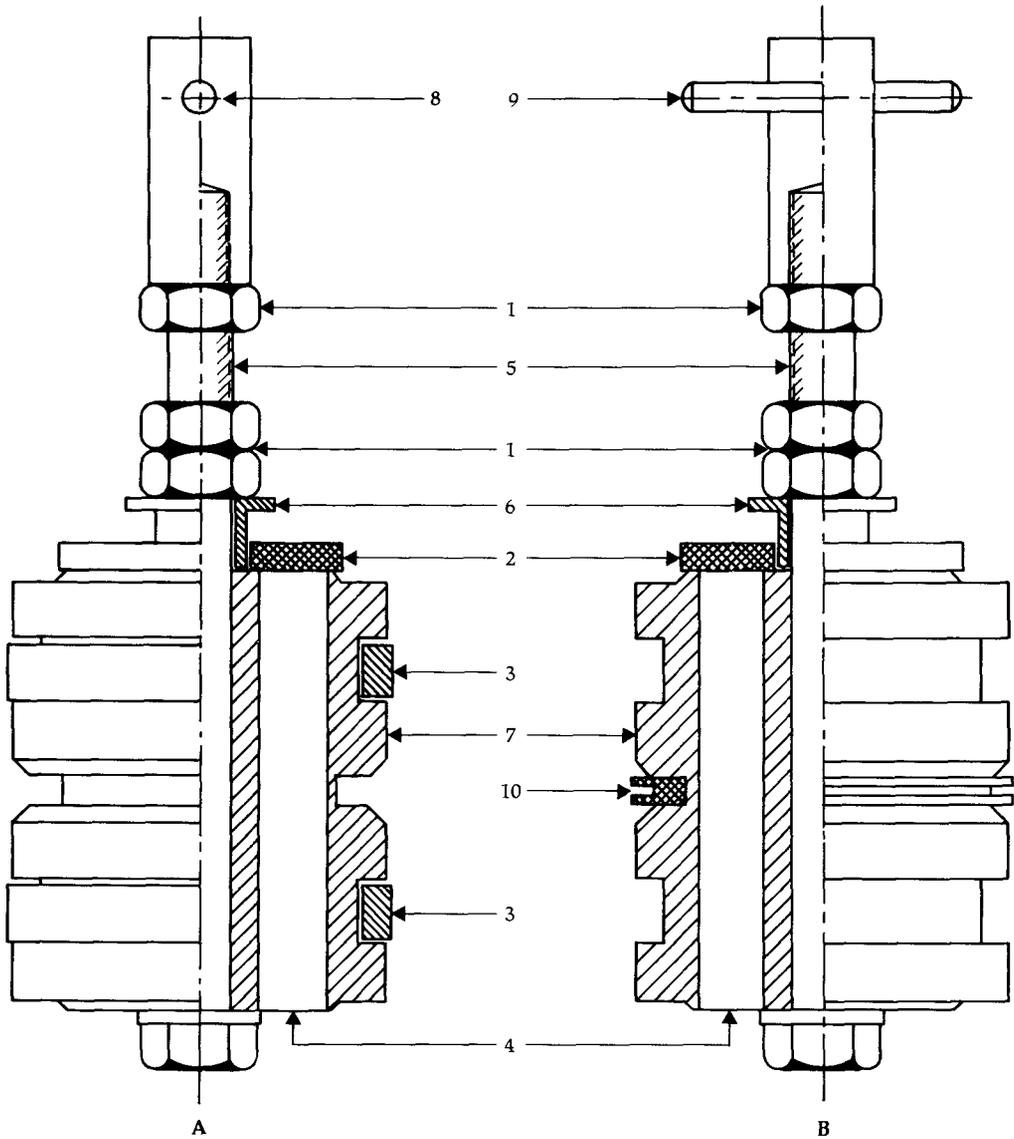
Assemblage du piston (A) et clapet de pied récupérable (B) : 1) contre-écrous ; 2) clapet de soupape (en caoutchouc naturel) ; 3) segments de piston (en polyéthylène) ; 4) six trous percés à égale distance ; 5) boulon ; 6) butée de soupape ; 7) plastique PVC ; 8) trou pour la goupille de fixation ; 9) goupille de récupération ; et 10) joint d'étanchéité en caoutchouc à rebord double.
